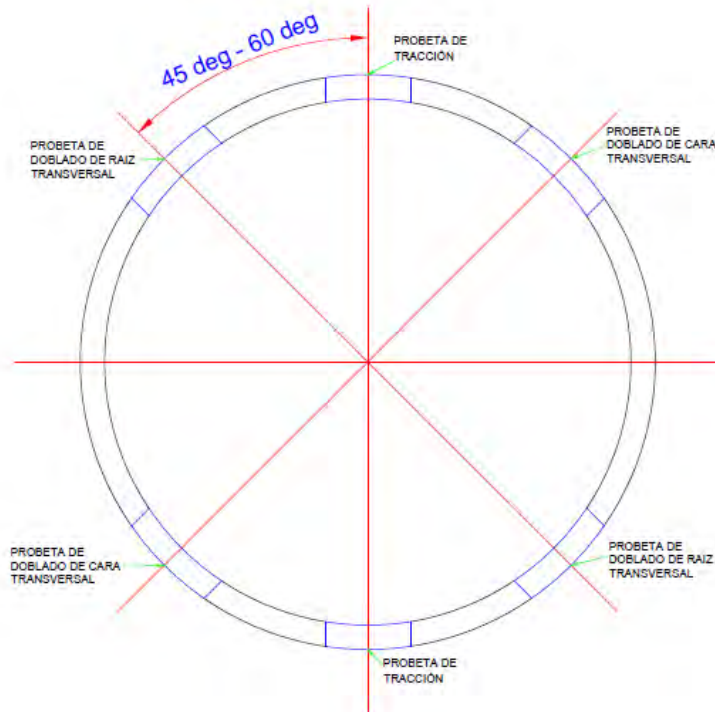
Cupón para calificación de soldadura-WPS N° 205
